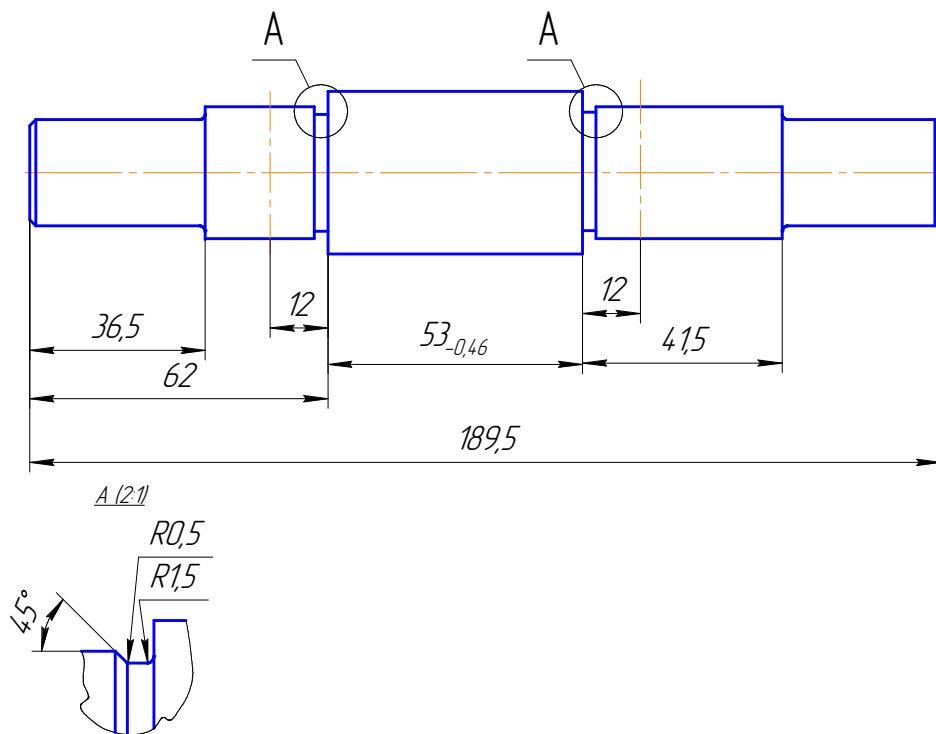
Схема задания размеров, обеспечивающая технологичность конструкции вала
